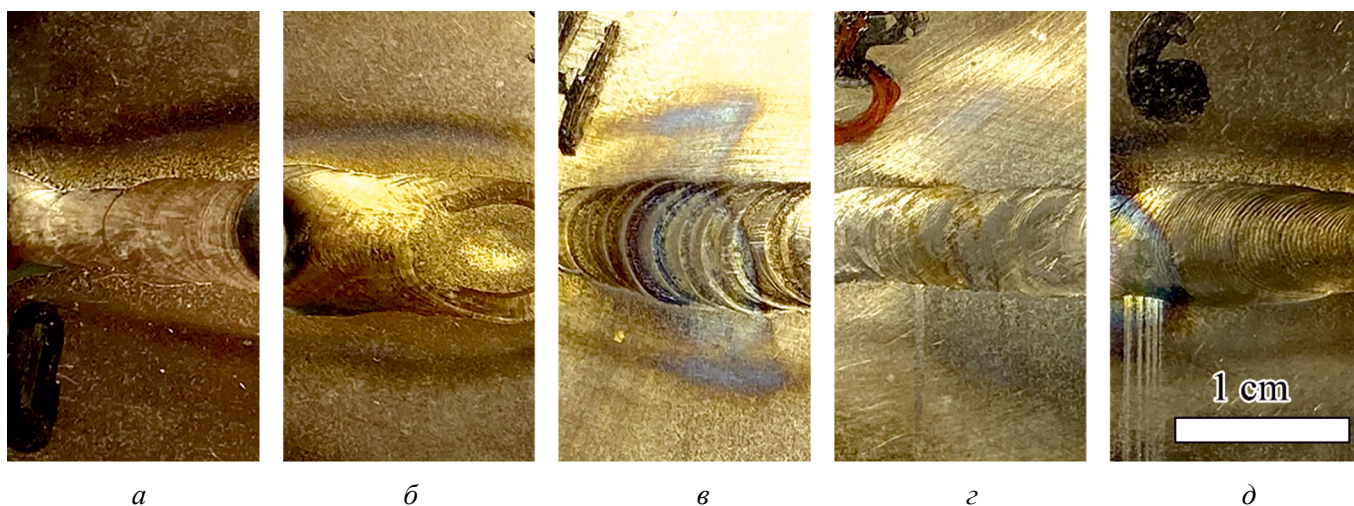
Внешний вид сварных соединений из сплава ВТИ-4, полученных TIG-сваркой при следующих условиях:
